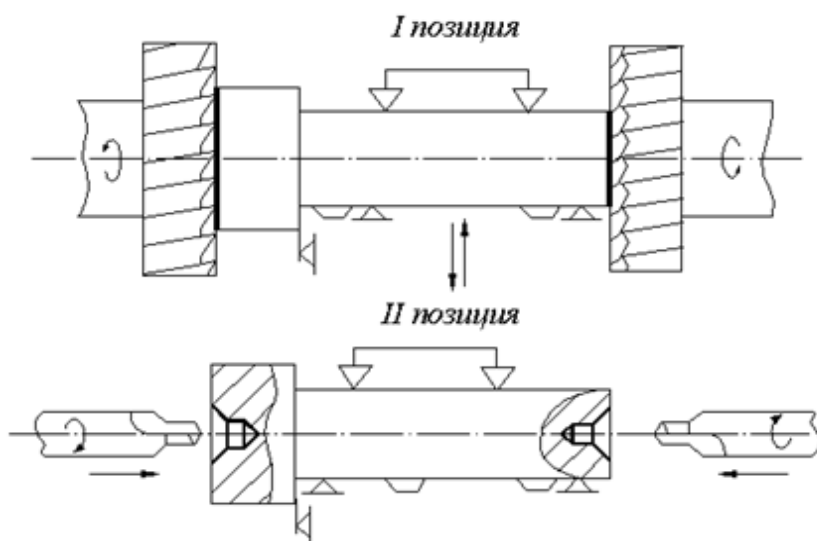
Схема обработки заготовки на фрезерно-центровальном станке
